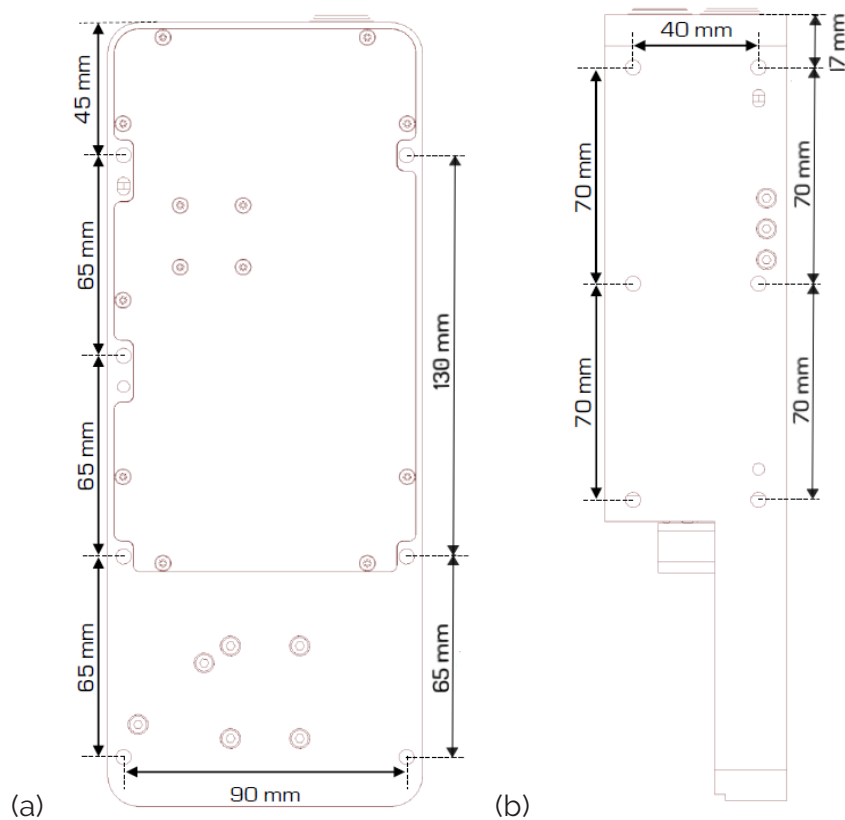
Abmessungen des heliInspect™ H8 Gehäusekörpers
